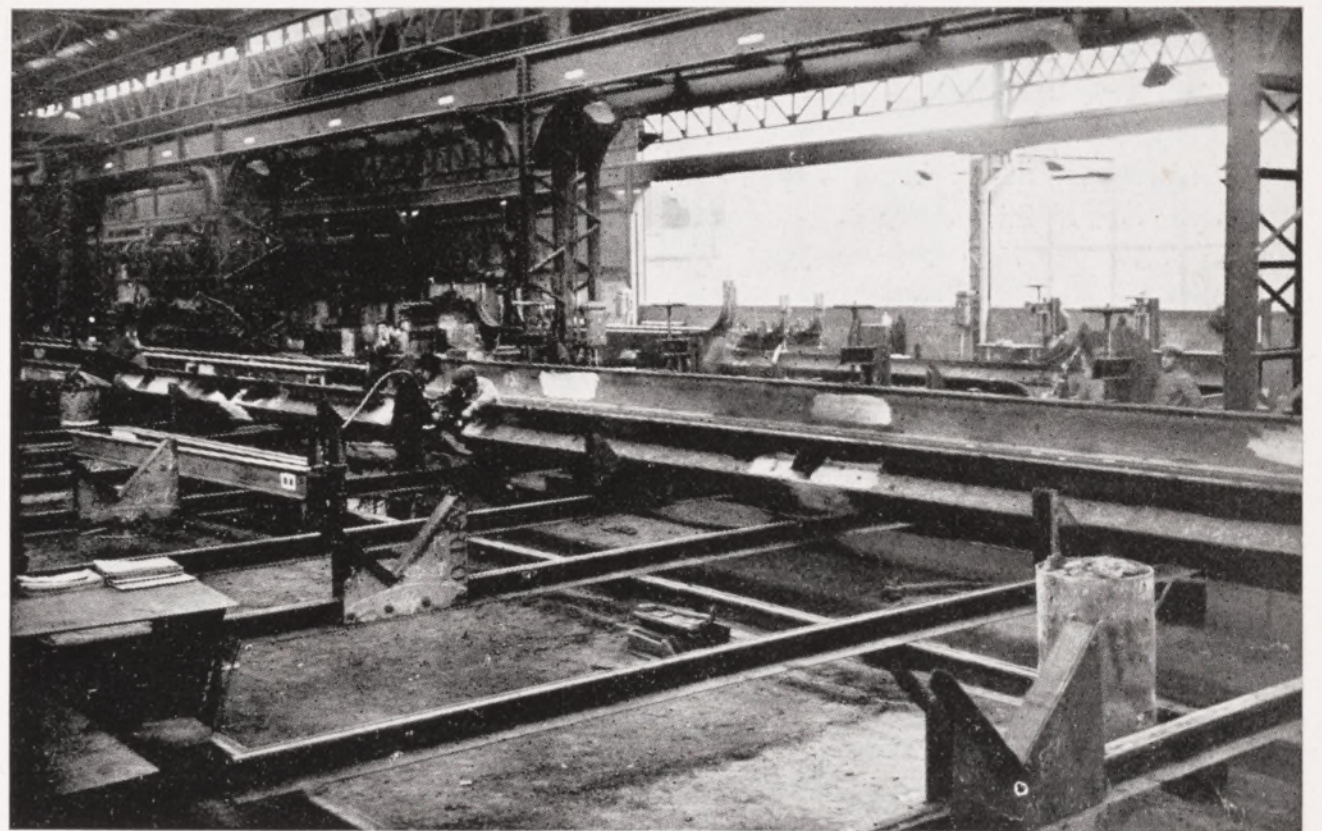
Contrôle d'un cordon de soudure à l'atelier.
